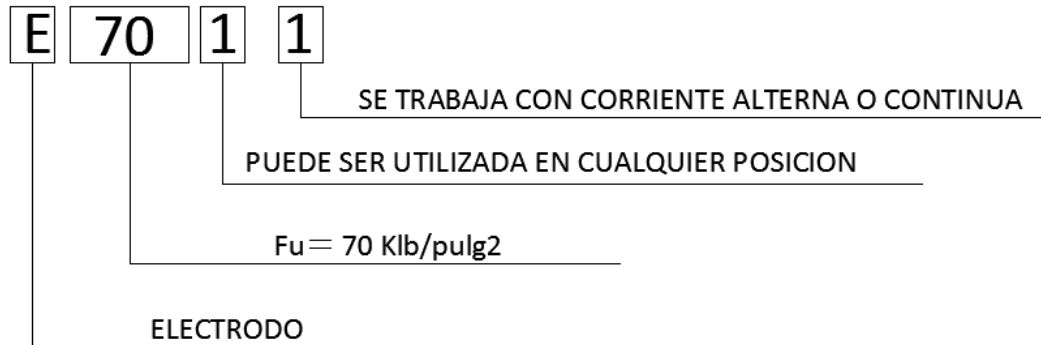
ESPECIFICACIONES DE LA SOLDADURA
